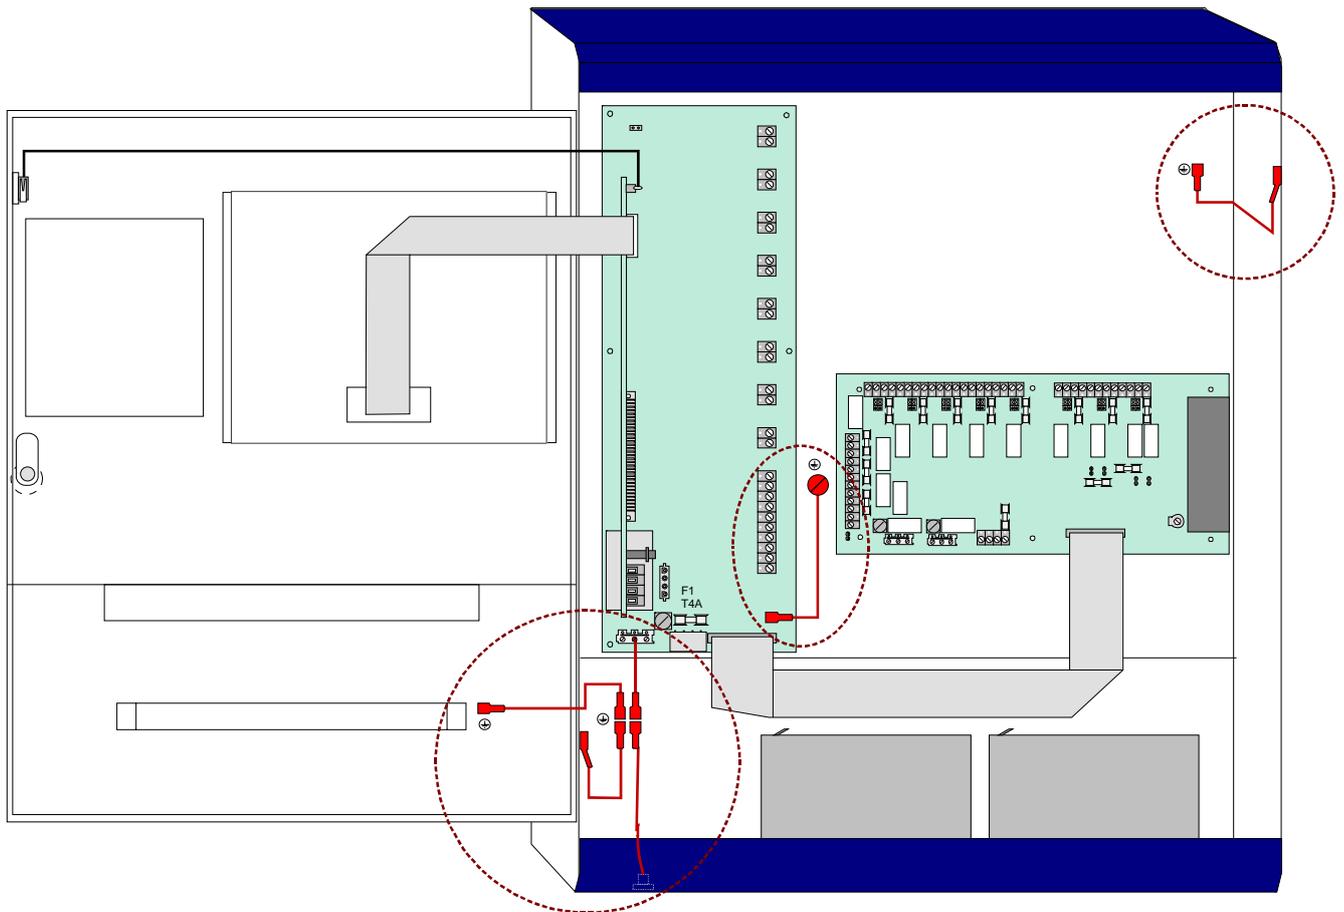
Conecte los cables de protección a tierra con la puerta abierta
